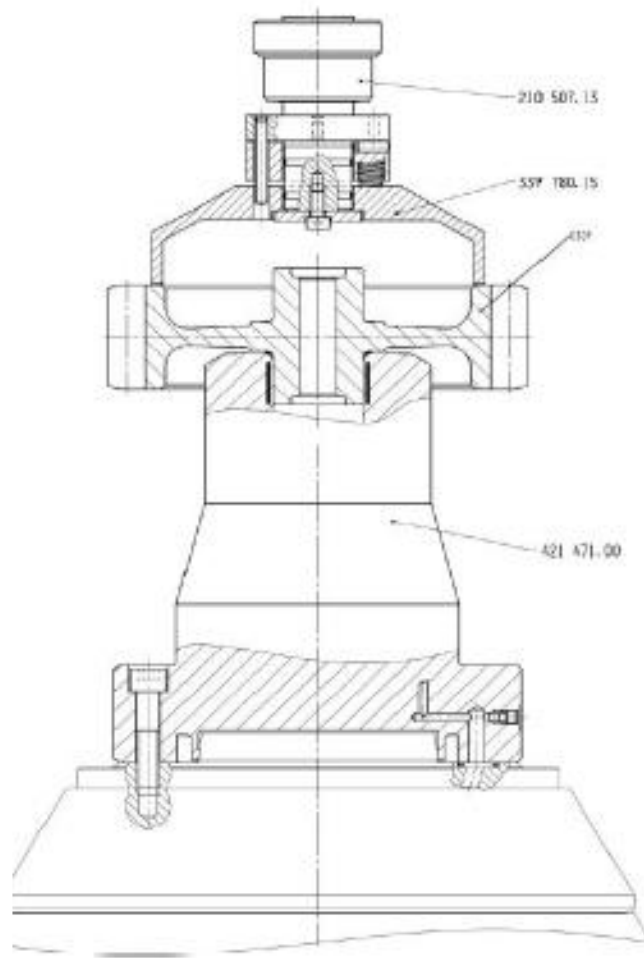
Гідравлічний пристрій для затискання зубчастого колеса
